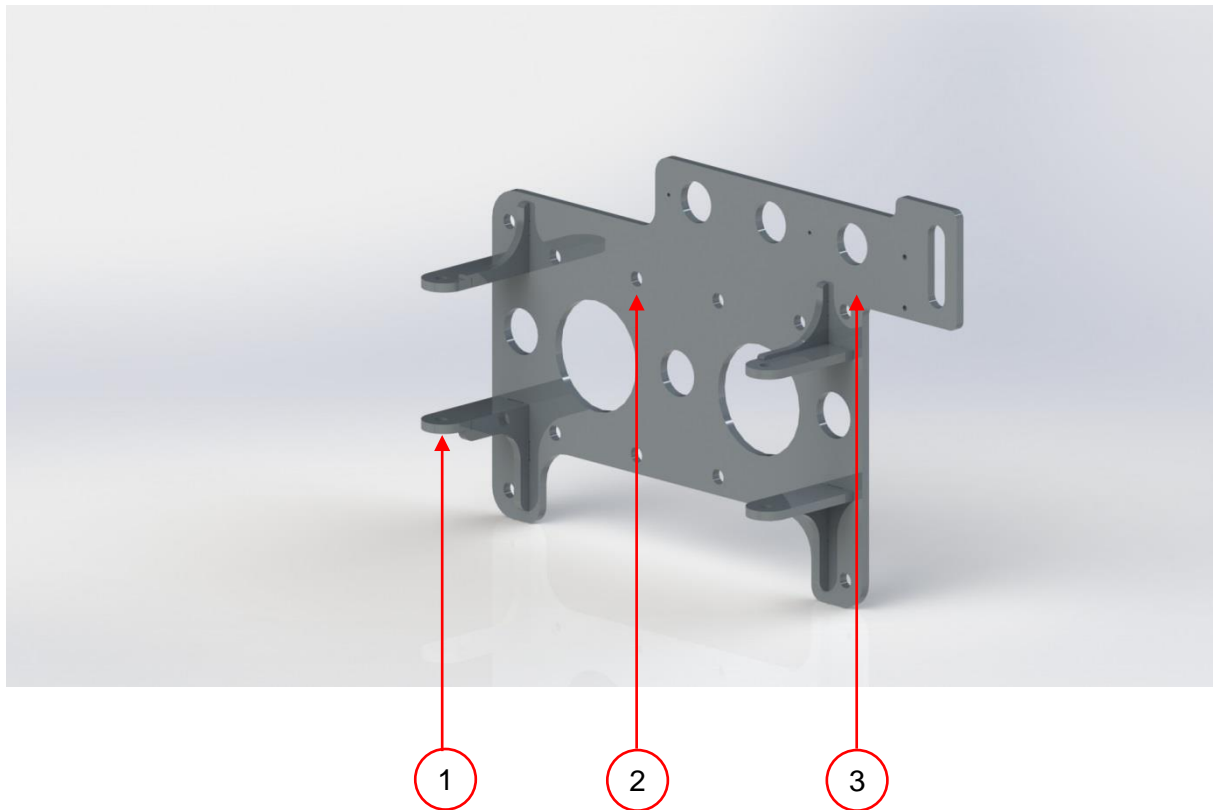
Übersichtsfoto der Komponenten für Werkzeugaufnahme
